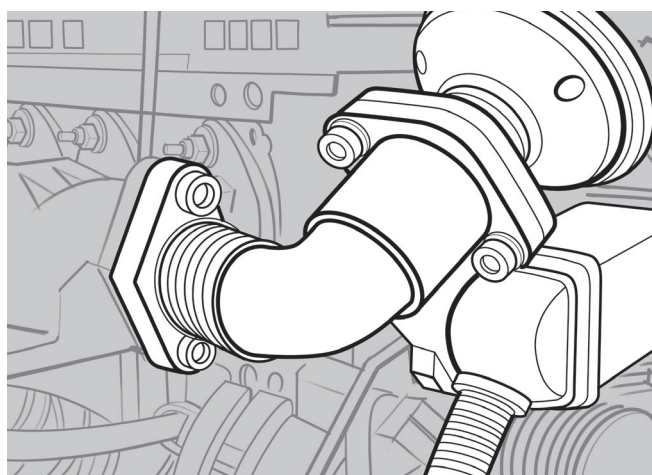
Al apretar los tornillos es imprescindible tener en cuenta que el montaje se produzca sin tensión
